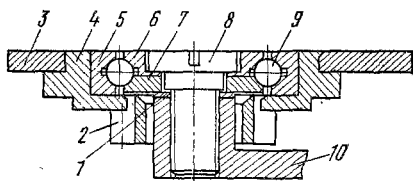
Схема шарикоподшипника в часах «Луч» 1816 с автоподзаводом пружины:
